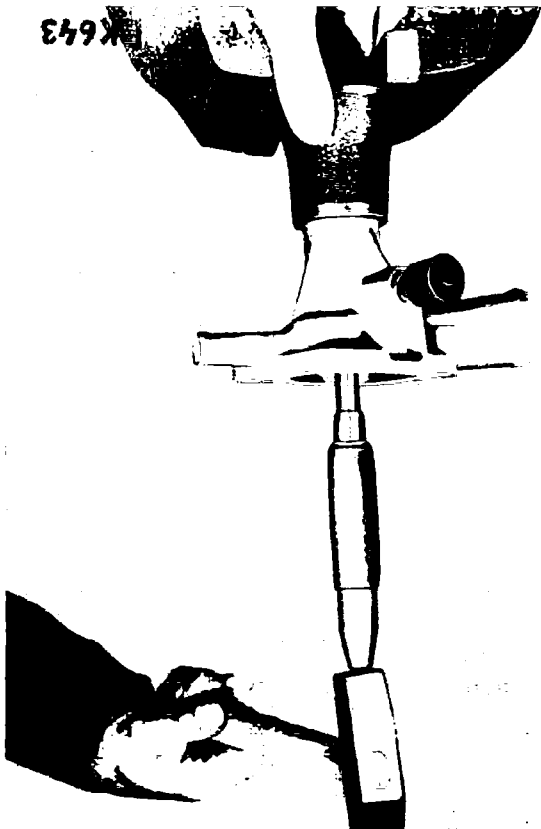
Heraus-schlagen der Wasserpumpen-lager mit Hilfe des Montagedorms MP 1-122
